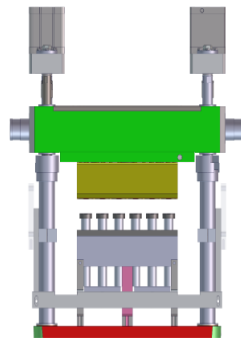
Schéma de presse soudure [31]
